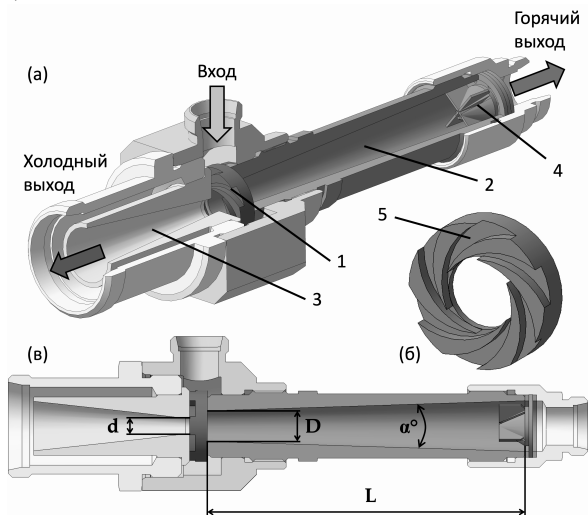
Схема и основные размеры вихревой трубы: 1 - сопловой ввод; 2 - камера энергоразделения; 3 - диффузор холодного потока; 4 - развихритель горячего потока с дроссельными отверстиями; 5 - сопловой сужающийся канал.
